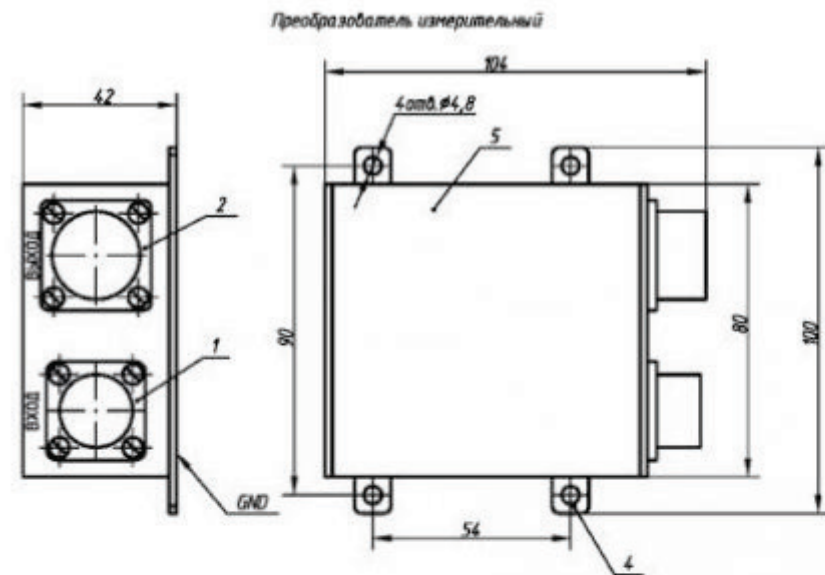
Габаритные и установочные размеры датчика вибрации трехкоординатного ДВА-ИЗ:
